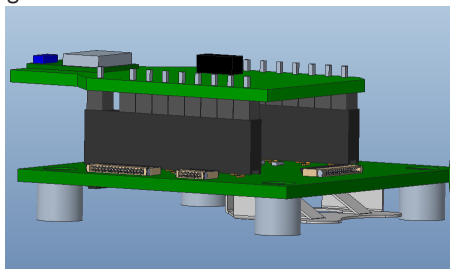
Elektronik- und Sensorikkomponenten im Werkzeug (Entwurf)
